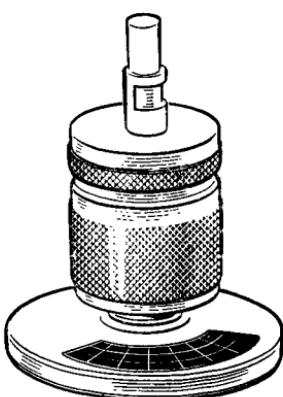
Прибор для проверки упругости пружины топливного насоса
